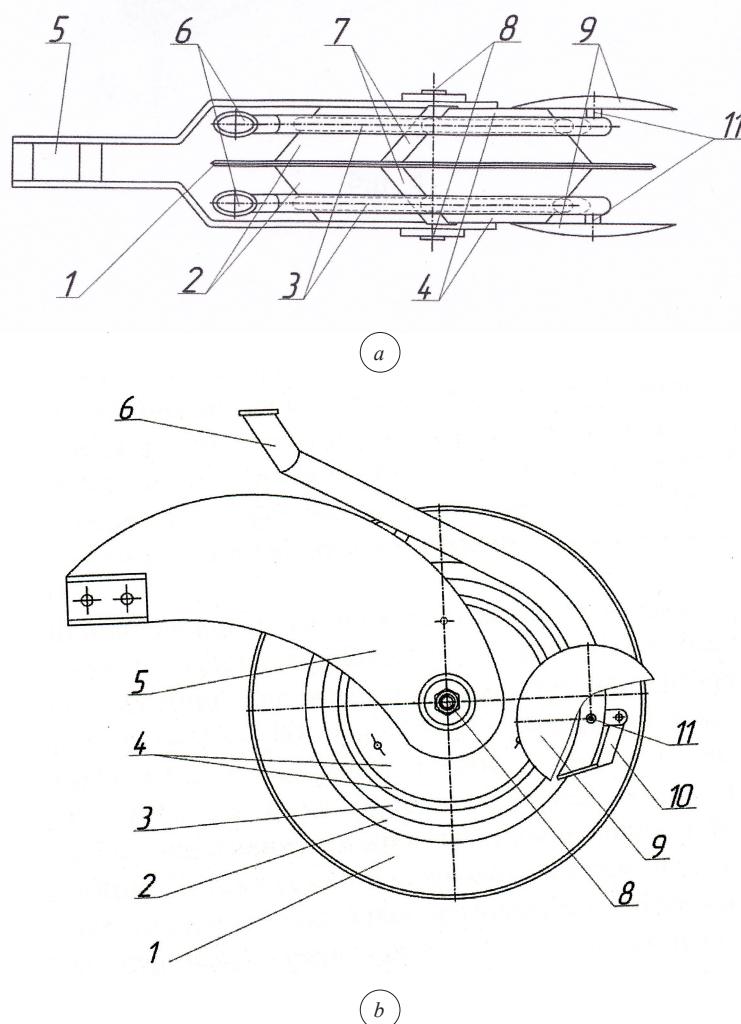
Комбинированный однодисковый сошник с двусторонними ребордами и сферическими дисковыми загортачами для узкорядного посева: *a* – вид сверху; *b* – вид сбоку; 1 – плоский диск; 2 и 4 – реборды; 3 – бороздкообразователи; 5 – корпус; 6 – семянаправители; 7 – чистик; 8 – ось; 9 – сферический диск; 10 – клапан; 11 – оси
